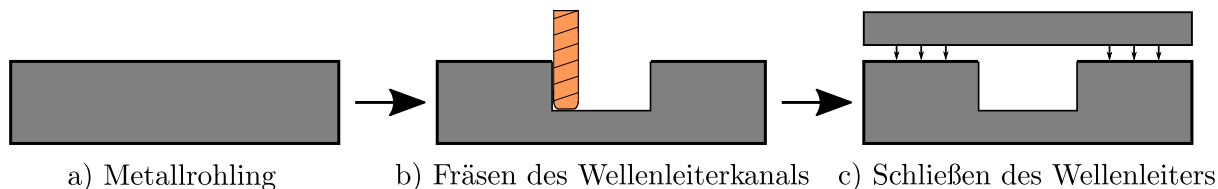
Schematische Darstellung der Fertigung von in Metall gefrästen Rechteckhohlleitern. Im ersten Schritt wird in einen Metallrohling (a) mit Hilfe einer CNC-Maschine ein Kanal mit rechteckigem Querschnitt gefräst (b). Im Anschluss wird lediglich ein weiterer Metallkörper nach dem Splitblock-Prinzip auf dem zuvor bearbeiteten Metallkörper mit einem beliebigen Verfahren befestigt (c).
